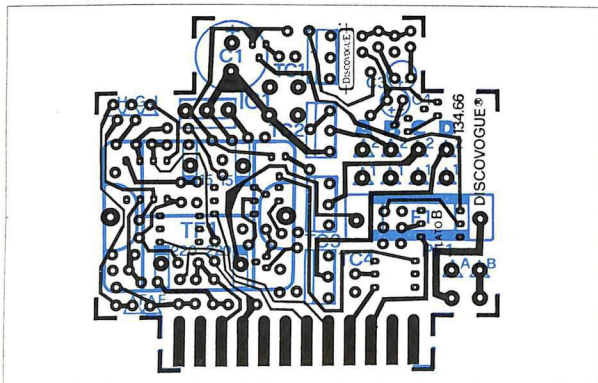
Pista conduttrice del lato B del circuito 134.66 con montaggio dei componenti sul lato B.
